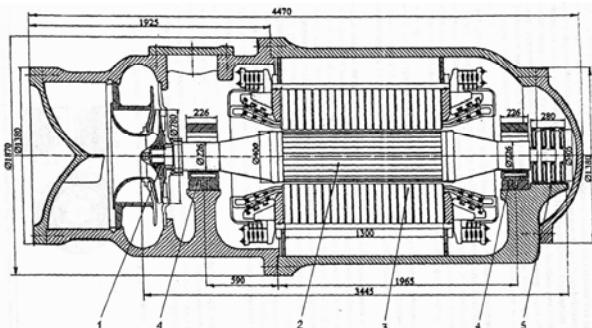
Газоперекачивающий агрегат помещаемый в трубопровод: 1 – рабочее колесо; 2 – ротор; 3 – электродвигатель; 4 – опорные подшипники с газовой смазкой; 5 – упорный подшипник
